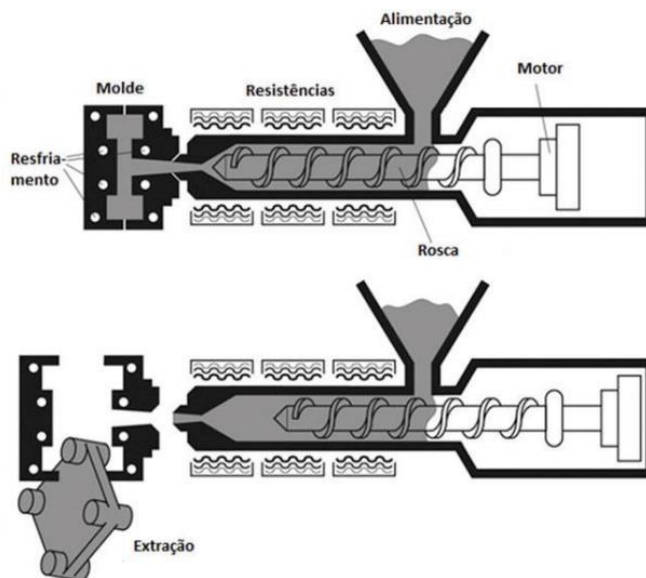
Processo de moldagem por injeção. Fonte: www.abiplast.org.br/
